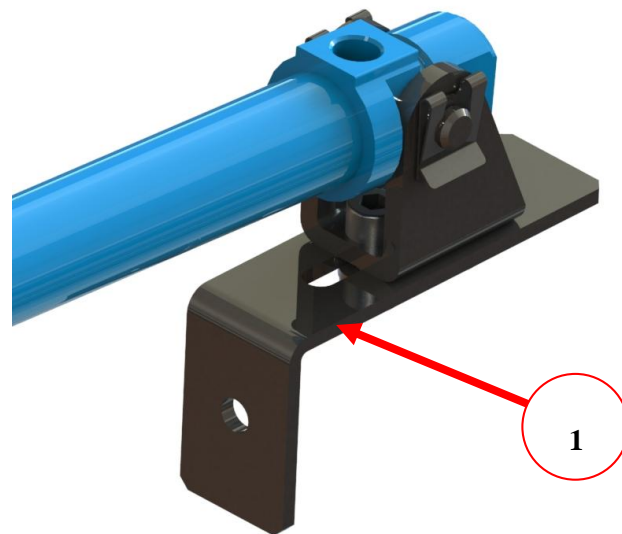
Cavalete de fixação do cilindro, fixo à chapa quinada com furo rasgado
